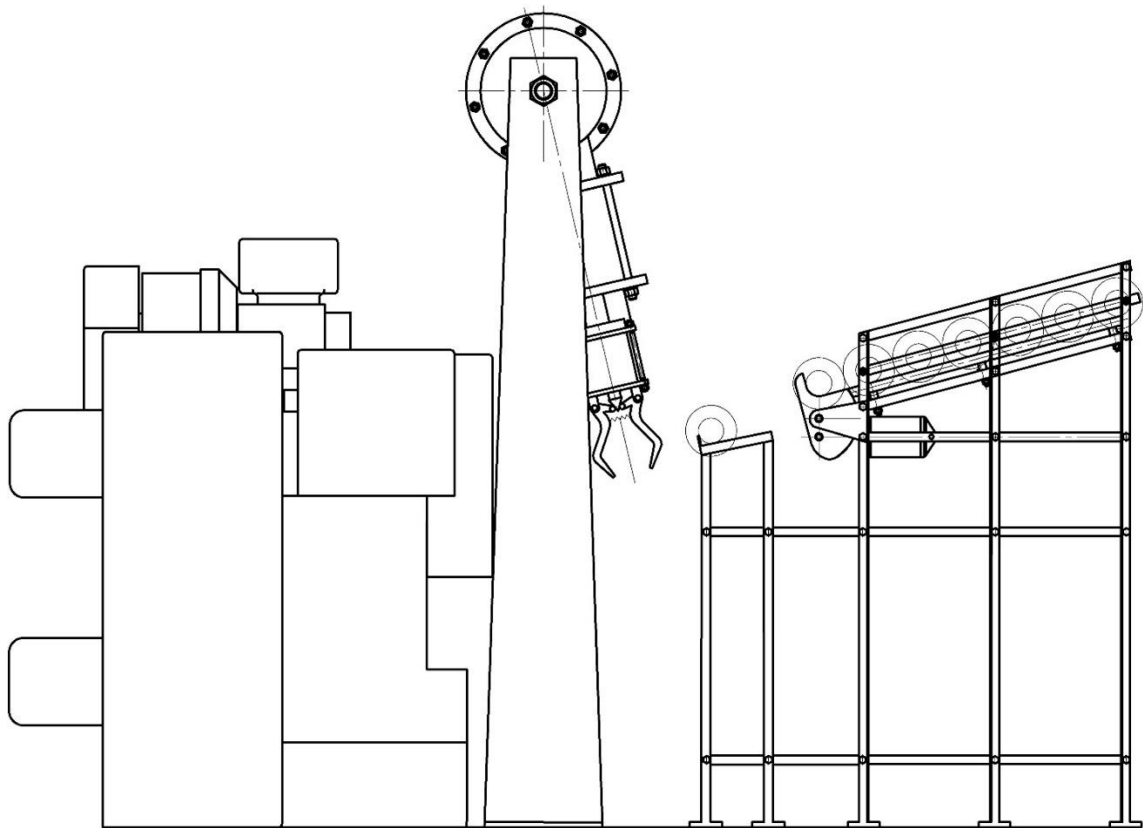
Компоувальне креслення завантажувального пристрою верстата
